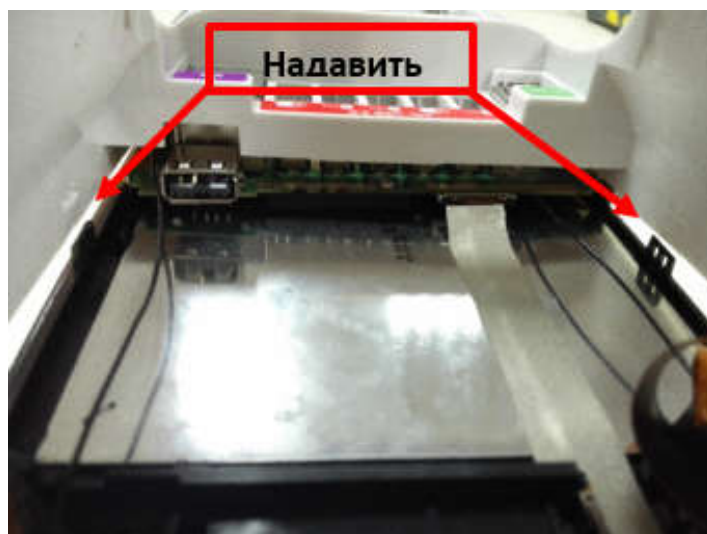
Пластиковые защёлки корпуса СТ и рамки сенсорного экрана.
